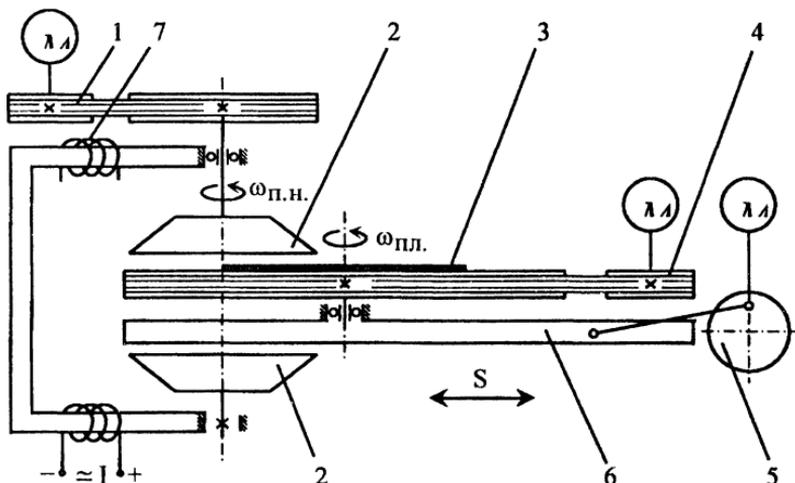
Схема магнитно-абразивной обработки кремниевых пластин: 1 – привод вращения полюсных наконечников; 2 – полюсные наконечники; 3 – обрабатываемая пластина; 4 – привод вращения пластины; 5 – привод подачи; 6 – каретка; 7 – электромагнитные катушки
